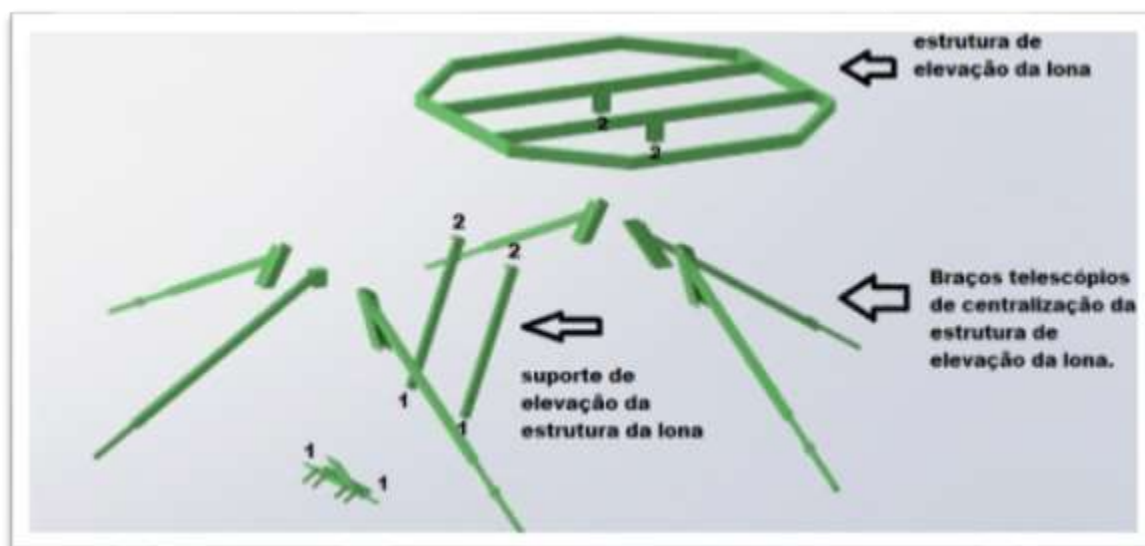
Vista explodida da estrutura de Elevação da Lona com Suportes.
